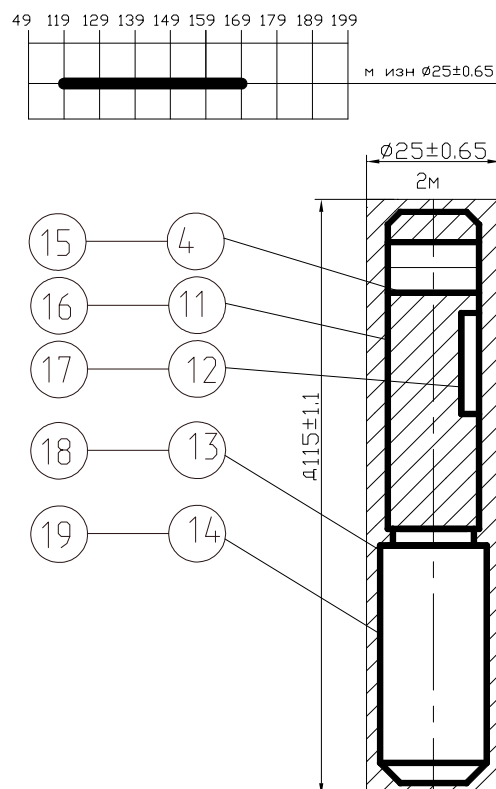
Преобразованный чертёж заготовки (вторая проекция)
